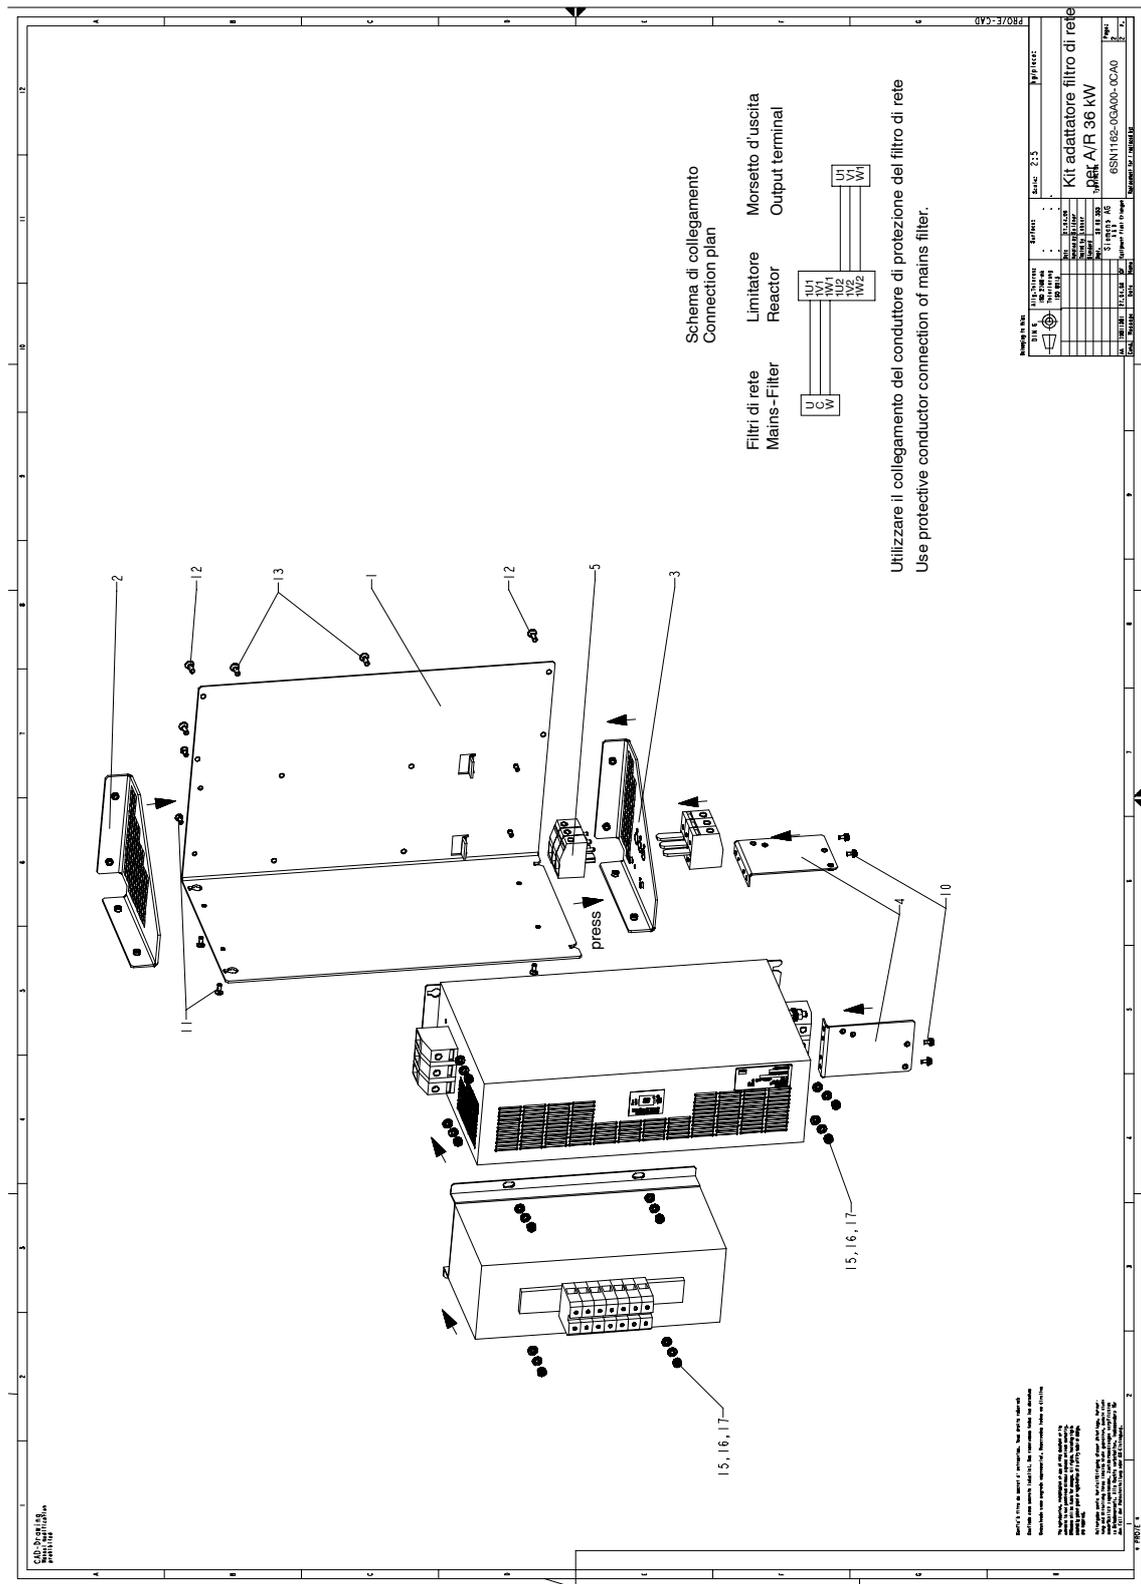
Kit adattatore filtro di rete per modulo E/R 36 kW, 6SN1162-0GA00-0CAx; montaggio
